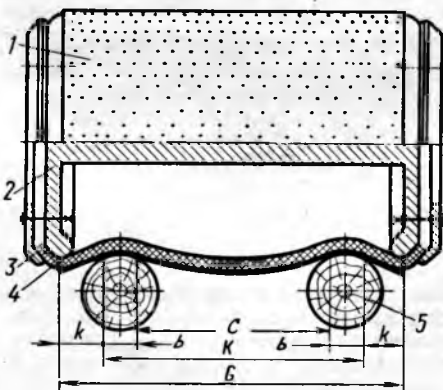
Шлифовальный инструмент в контакте с обрабатываемой заготовкой:
